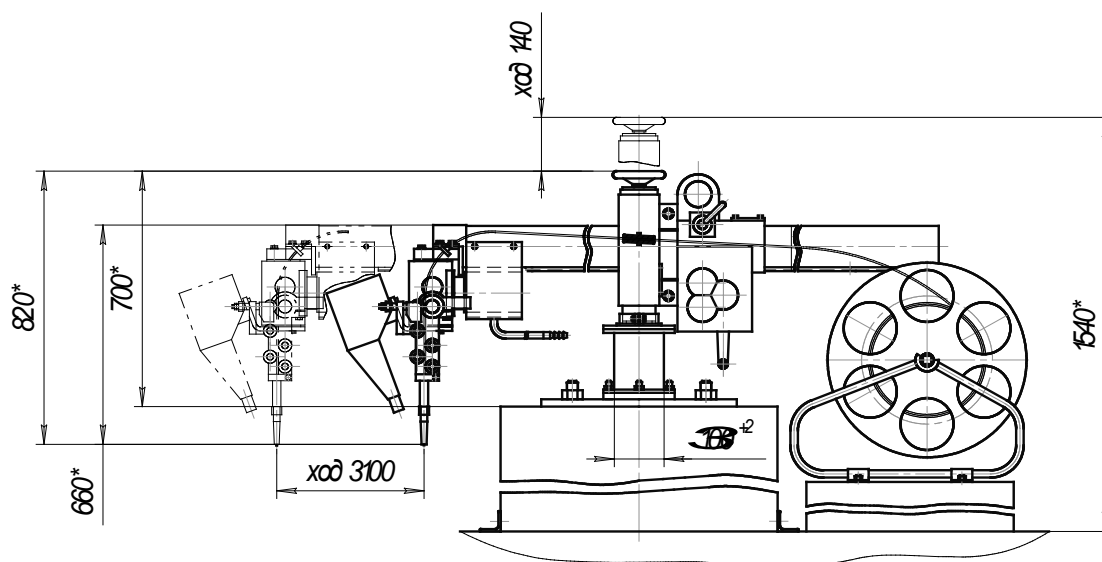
Установка для сварки (наплавки) внутренних швов обечаек
